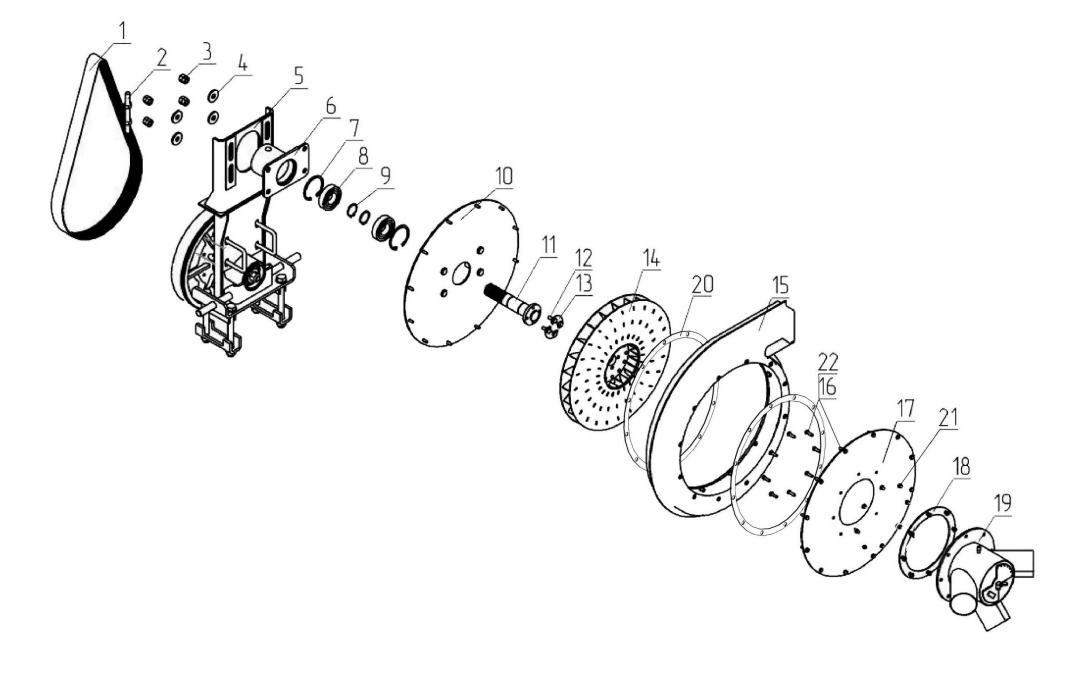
Вентилятор 509.046.8370А. Верхний вал
